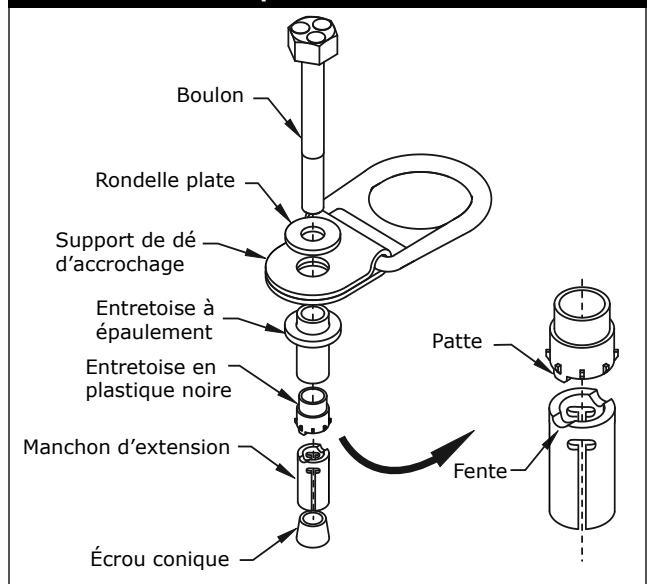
Assemblage du connecteur d'ancrage pour béton
